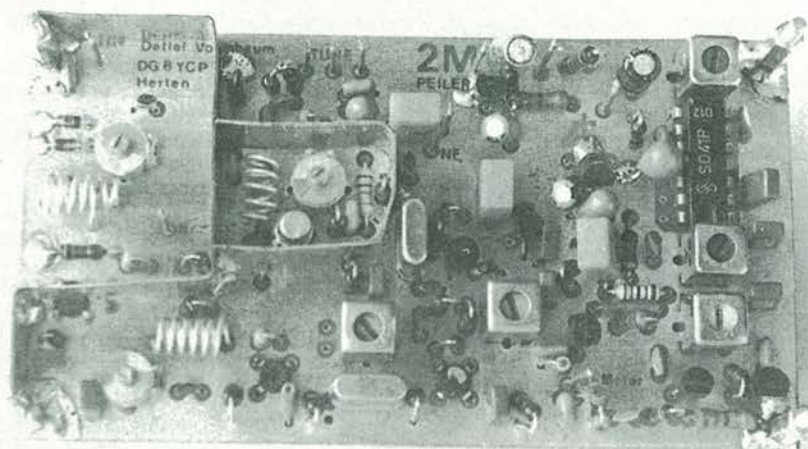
Basetta di alta frequenza completamente montata. I lamierini di schermo, visibili anche sul disegno della disposizione dei componenti, sono indispensabili.
